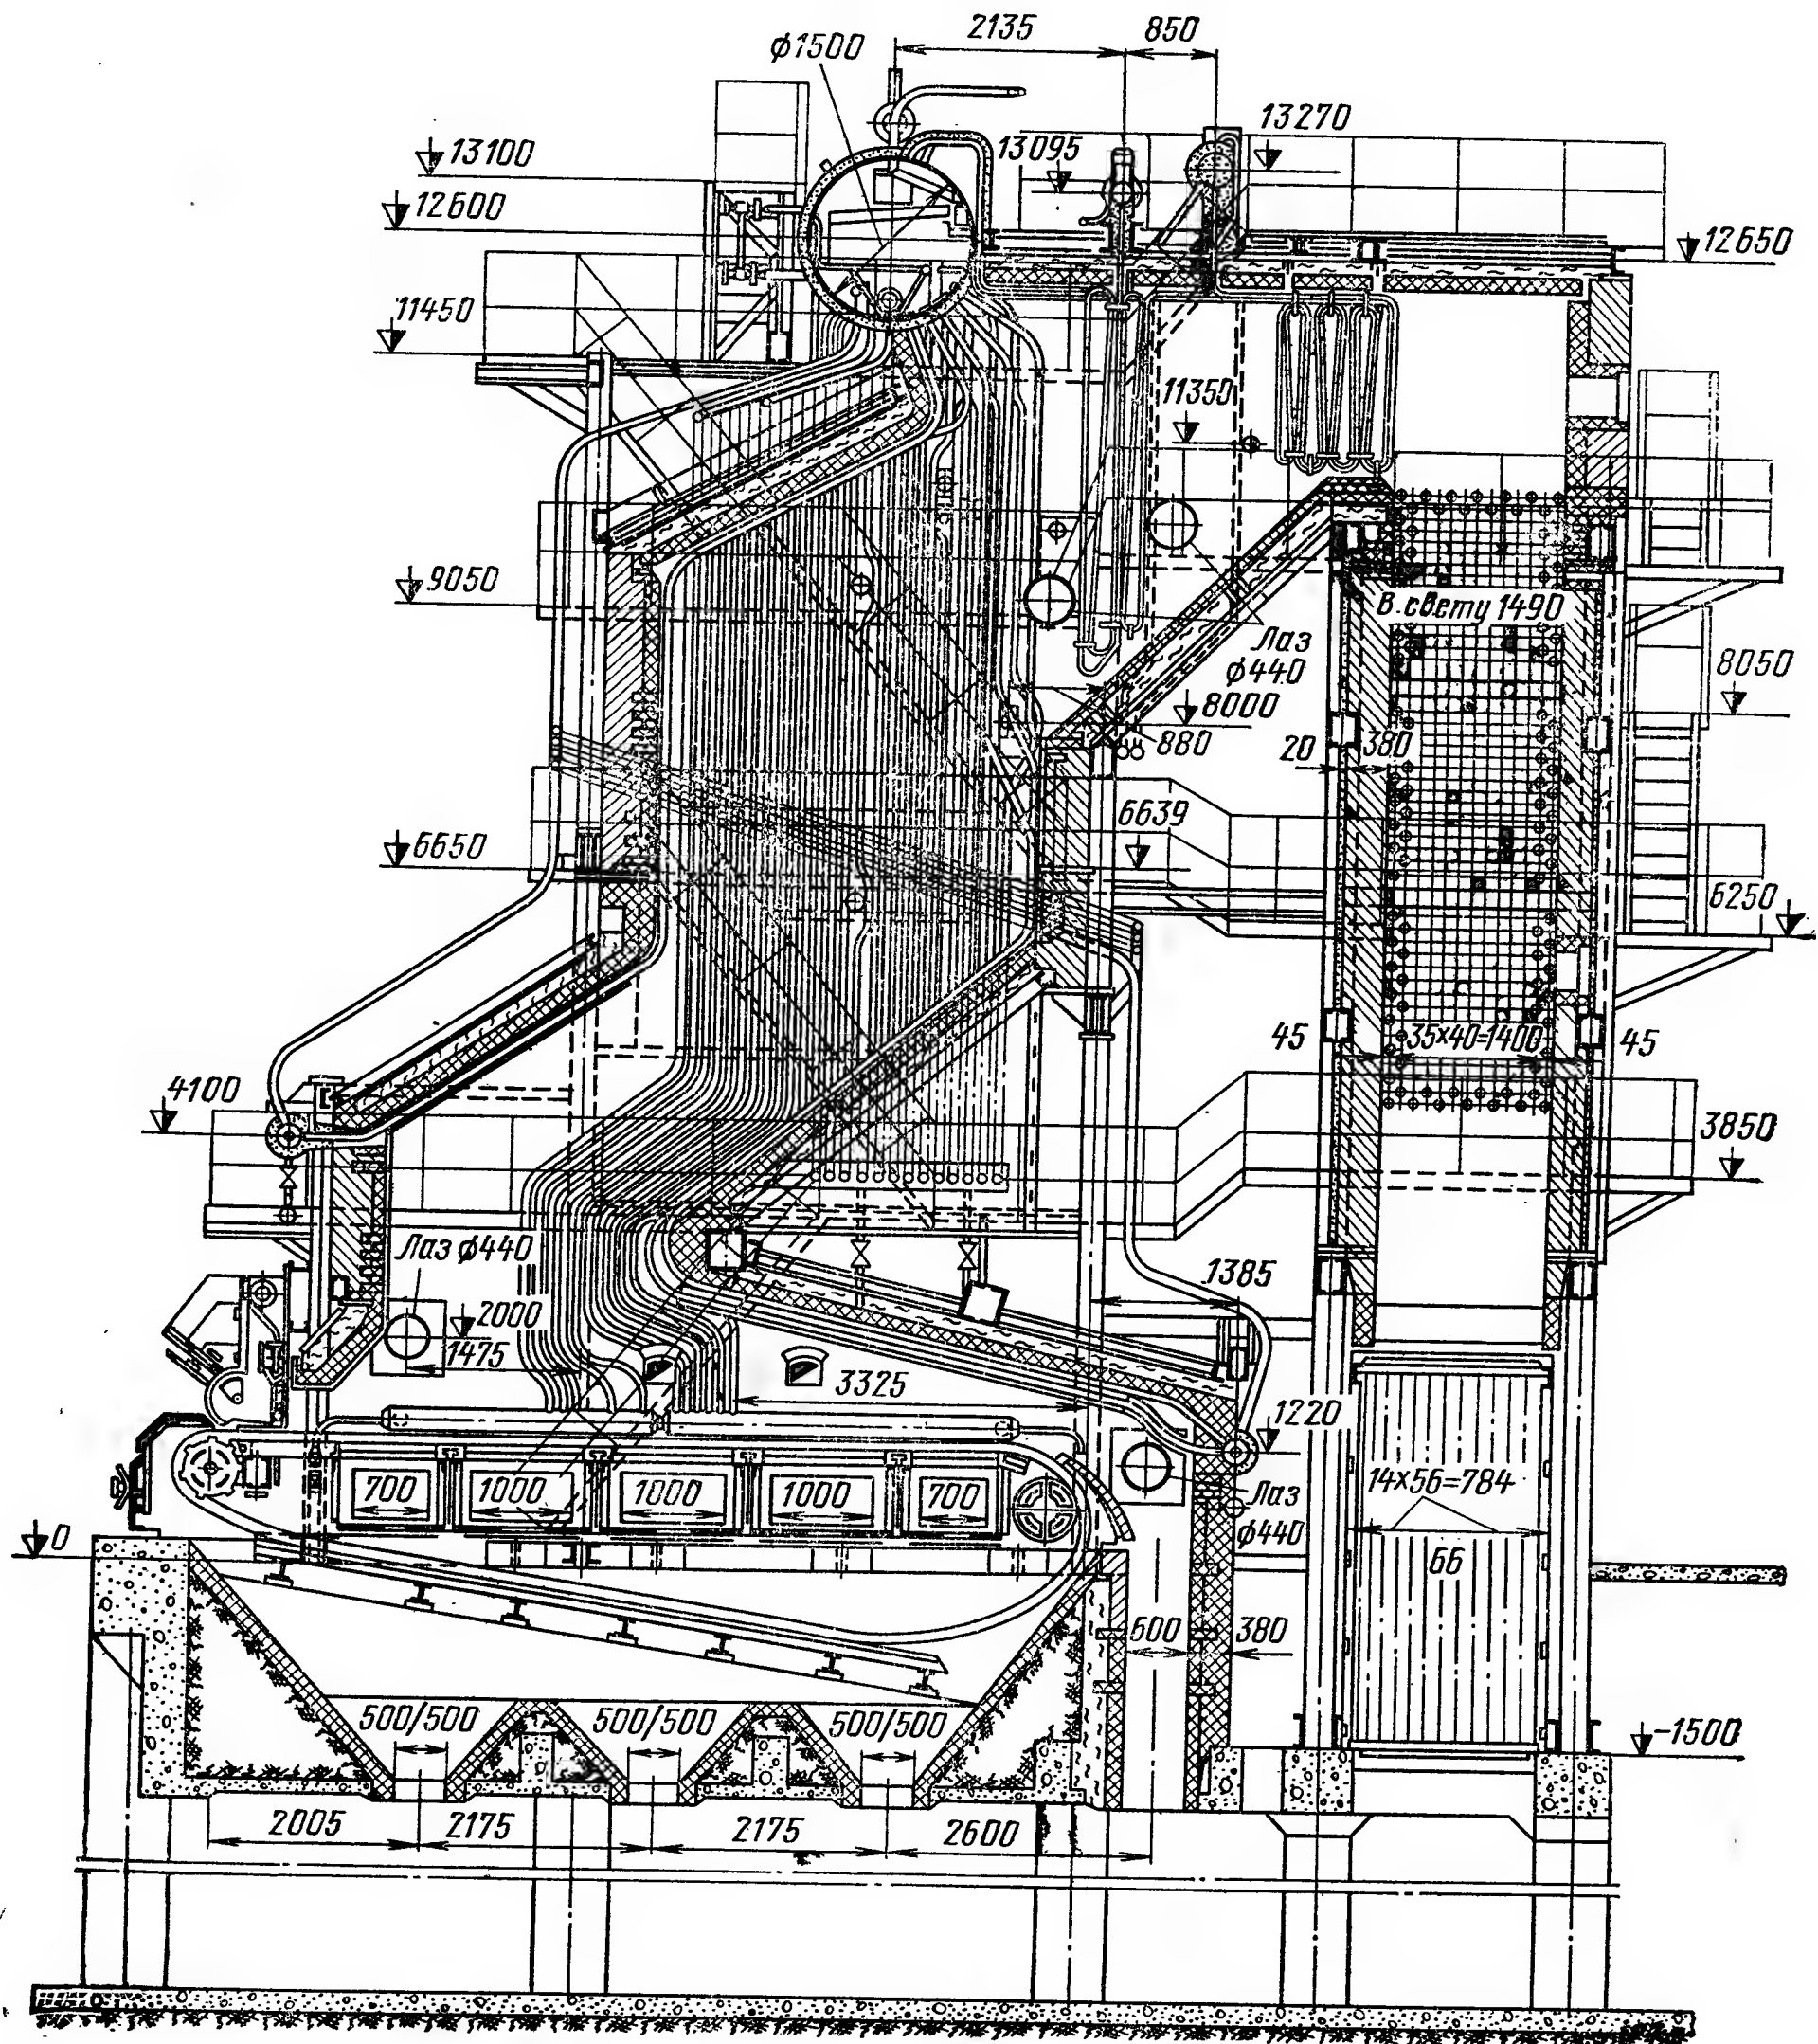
Котлоагрегат ТБ-35у с П-образной компоновкой поверхностей нагрева и слоевой топкой ЧЦР для сжигания антрацита.
